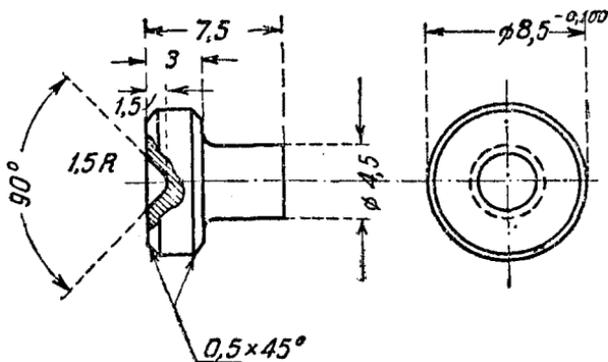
Дет. 6615. Вкладыш корпуса муфточки
